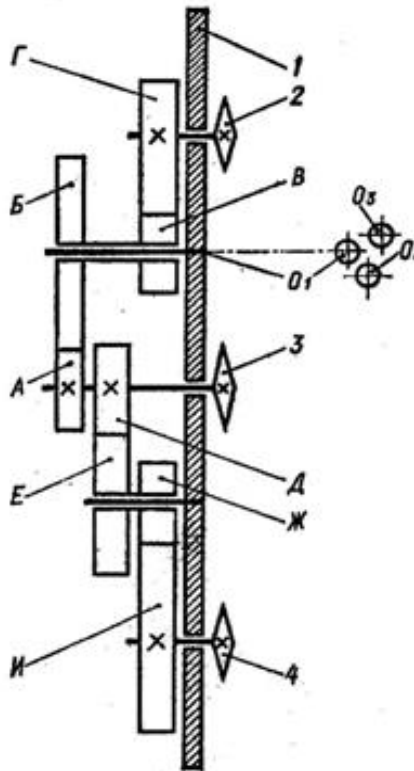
Схема редуктора сівалки СЗ-3,6:
